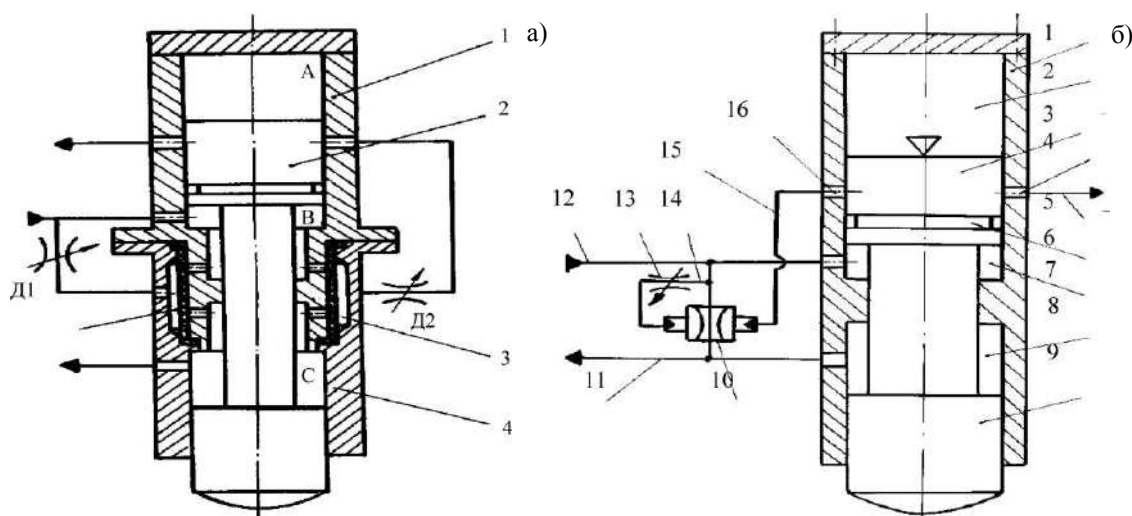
Конструктивные схемы беззолотниковых гидроударников: 1 - корпус; 2 - подвижные части; 3 - цилиндрический упругий запорно-регулирующий элемент; 4 - стакан
